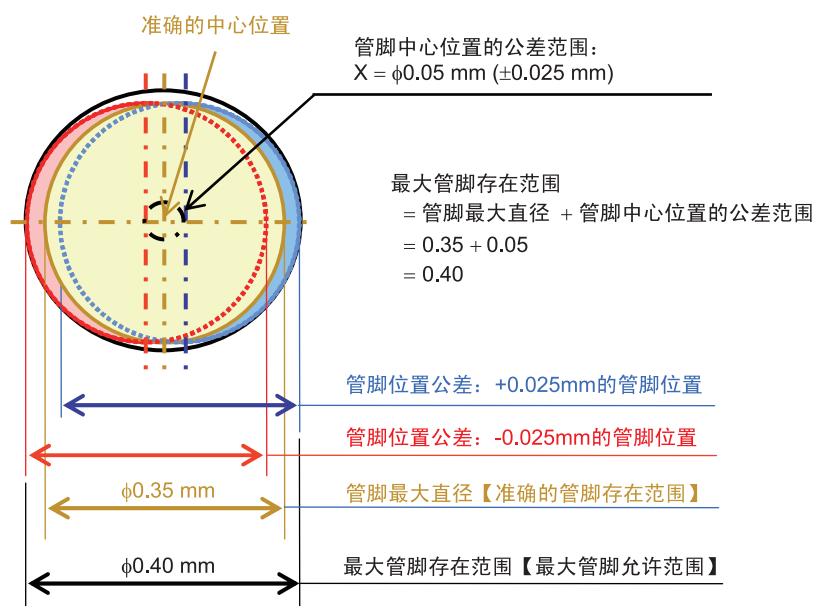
0.5 mm 节距 BGA 的管脚中心位置公差
